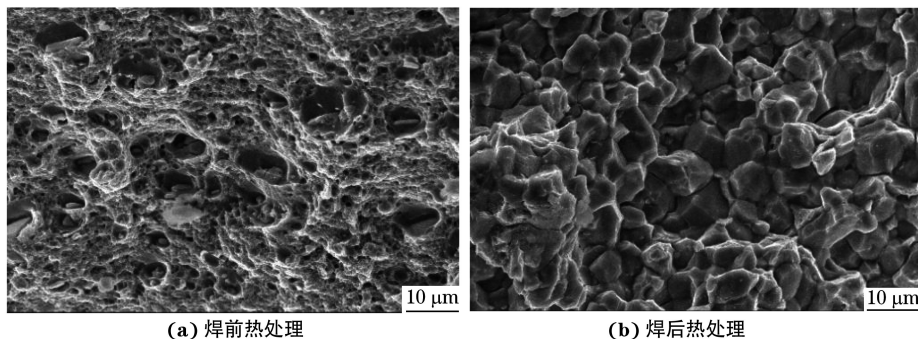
焊前和焊后热处理2#工艺制备得到焊接接头拉伸断口微观形貌
